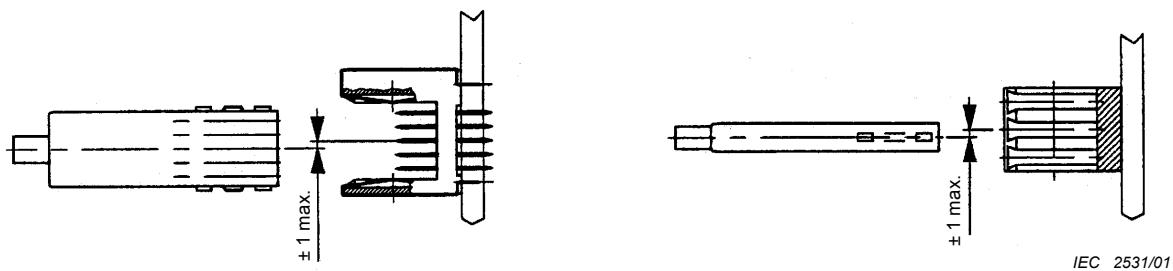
Défaut d'alignement permis en largeur et en hauteur
